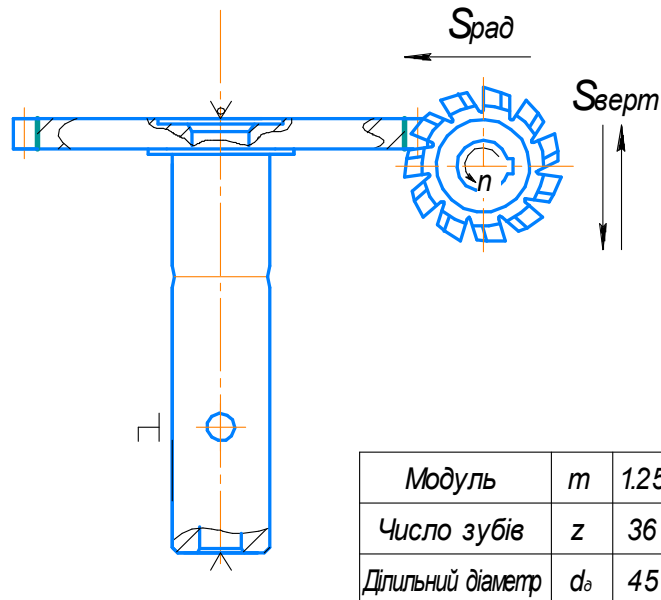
Схема обробки при зубофрезеруванні.
